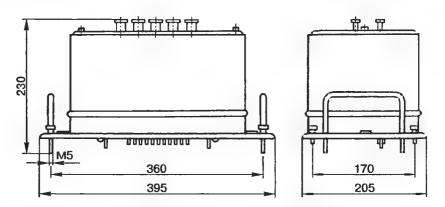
Габаритные и установочные размеры блоков типов БСК, ТПЧ, ФА
